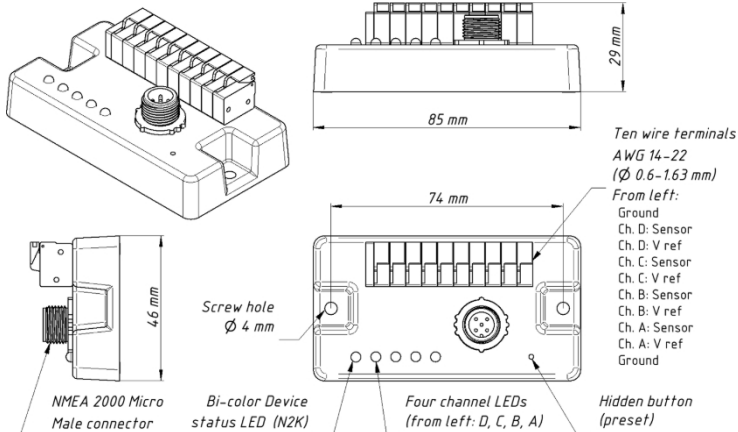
Чертеж адаптера для резервуара YDTA-04N
